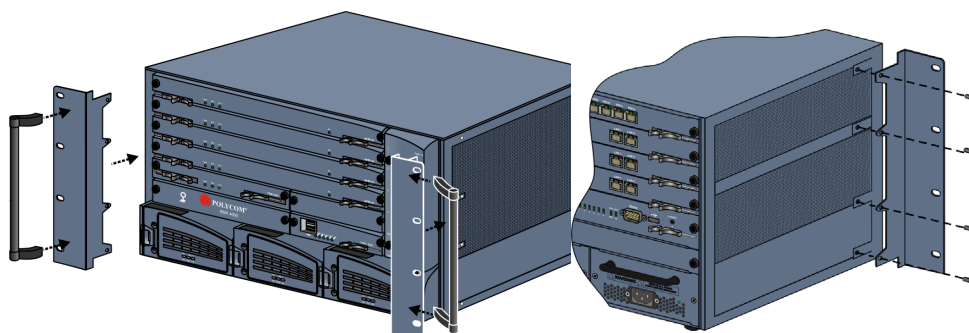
Installation des poignées et des supports et détail de la vue arrière de la fixation du support 23"
